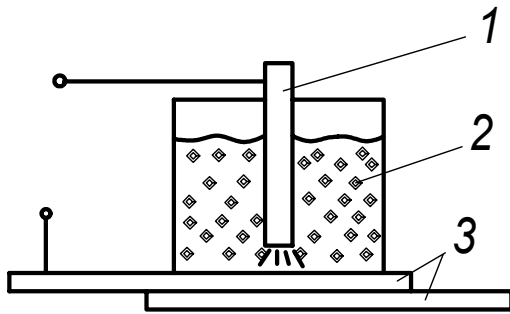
Схема сварки электрозаклепками:
